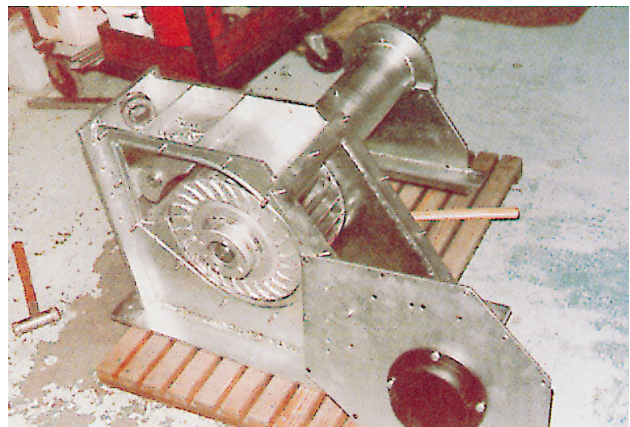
b) - Turbina a flusso passante di 15 kW in fase di montaggio.
